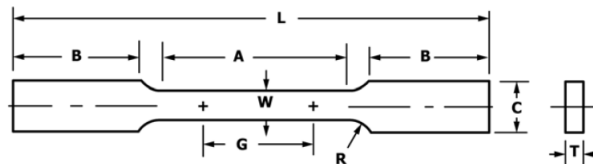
Corpo de prova padrão utilizado no ensaio de tração.
